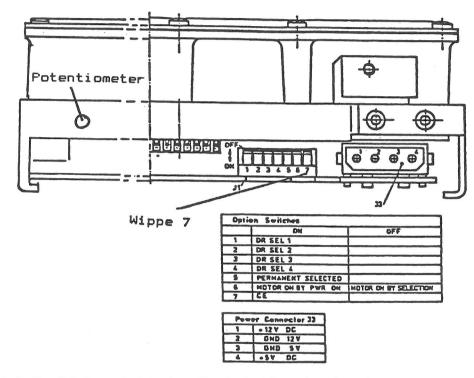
Rückansicht des Festplatten-Laufwerks
